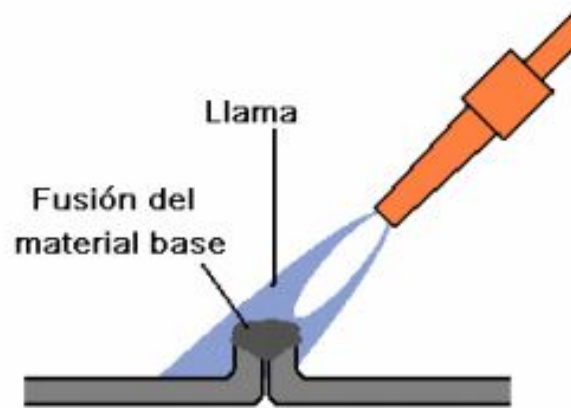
Soldadura sin material de aportación.[24]
